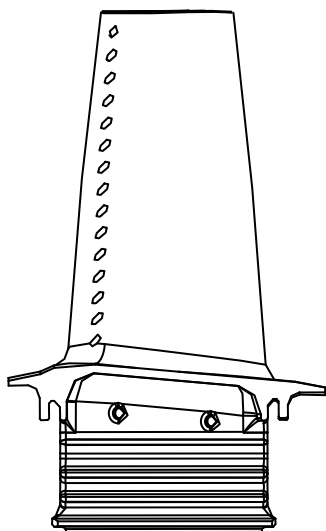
Рабочая лопатка ротора турбины ГТД
